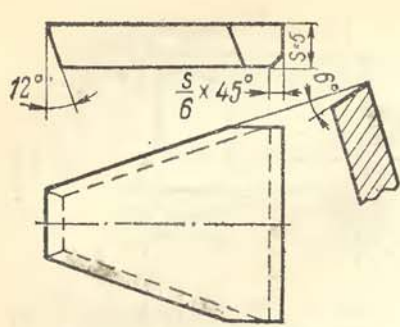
Твердосплавные напайваемые пластины типа 32190 и 32210 (ГОСТ 25412—82)
